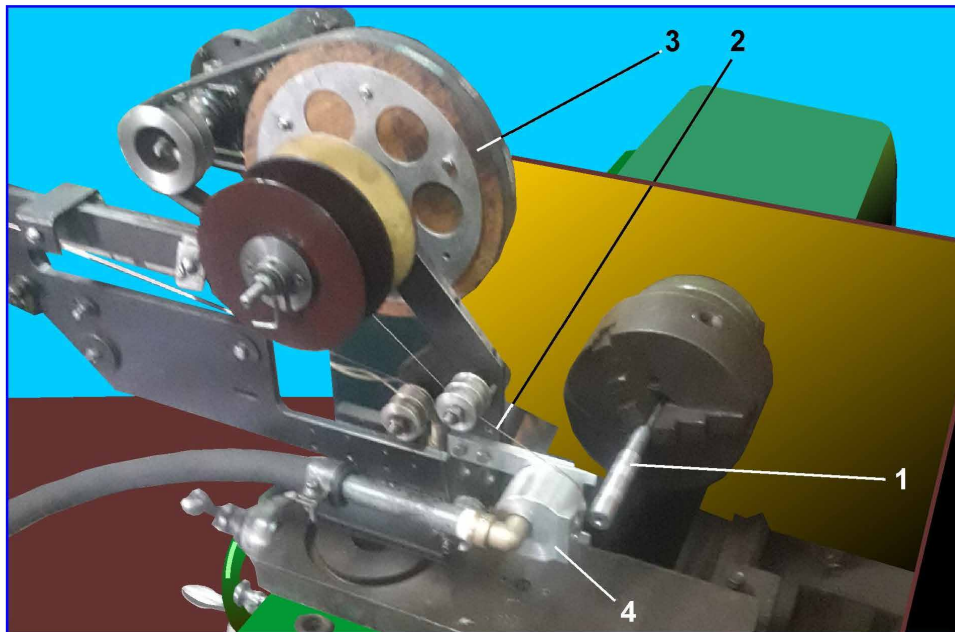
Експериментальний пристрій для обробки електричною дугою тіл обертання дротовим електрод-інструментом: 1 – електрод-заготовка; 2 – дротовий електрод-інструмент; 3 – механізм перемотування дроту; 4 – інструментальна головка
